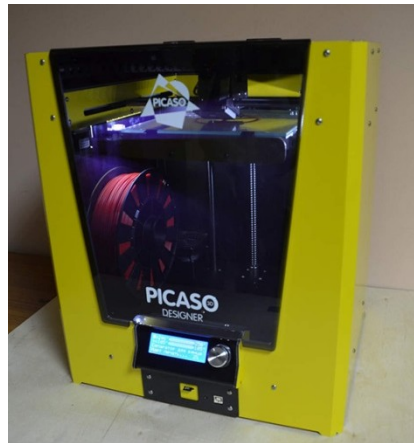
3D-принтер Picaso Designer и процесс печати
